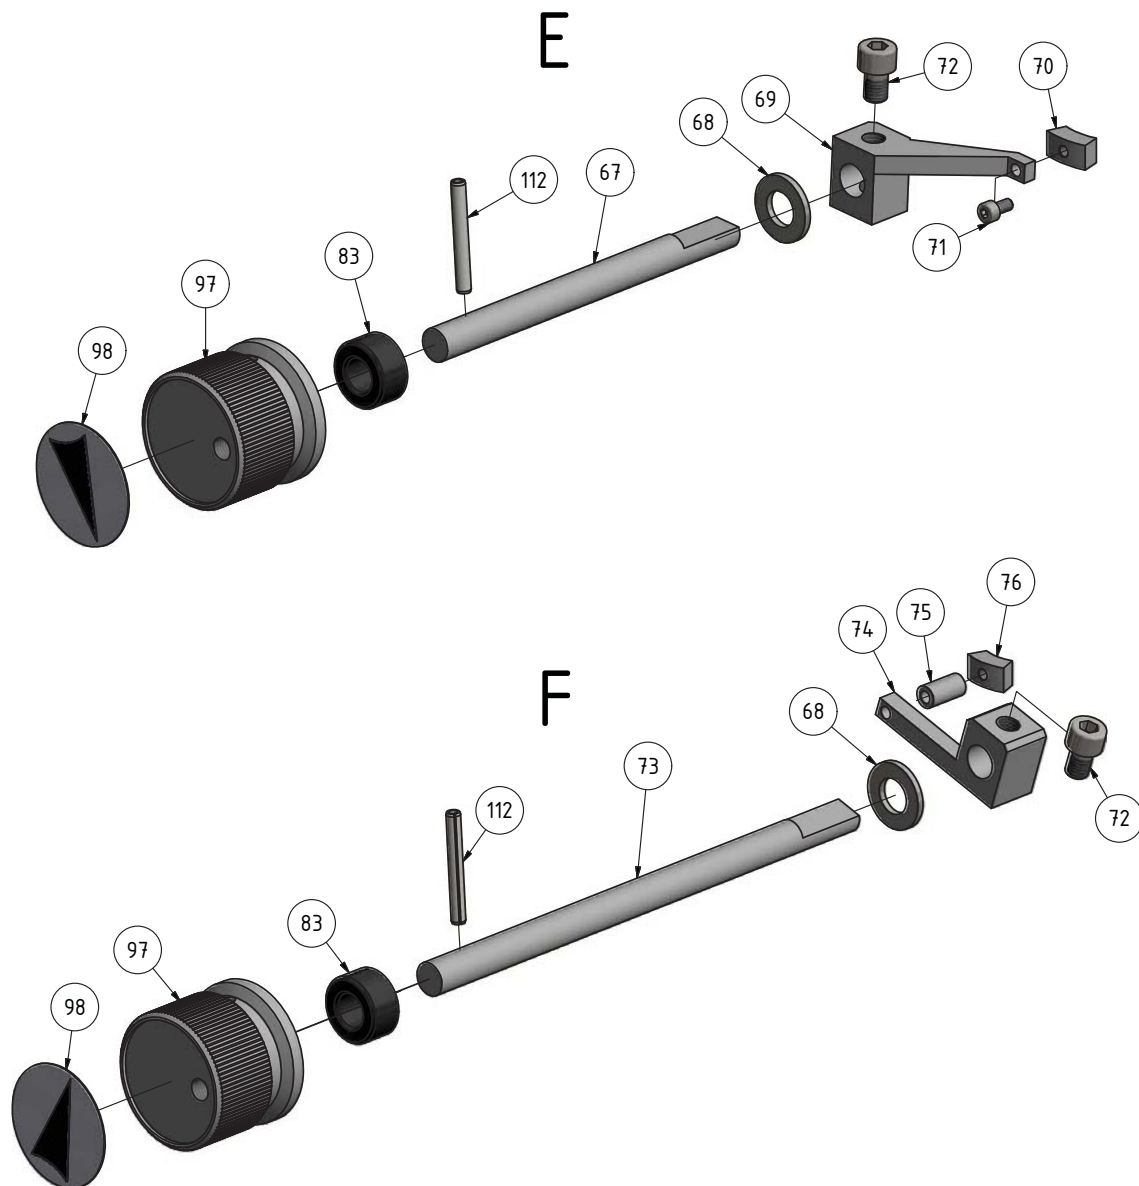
Fräskopf 4 von 6 - Milling head 4 von 6
